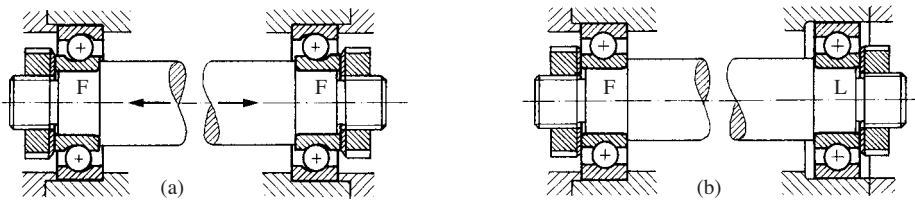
Arbres sur deux roulements à billes: (a) deux paliers fixes, montage hyperstatique; (b) un palier libre axialement.
